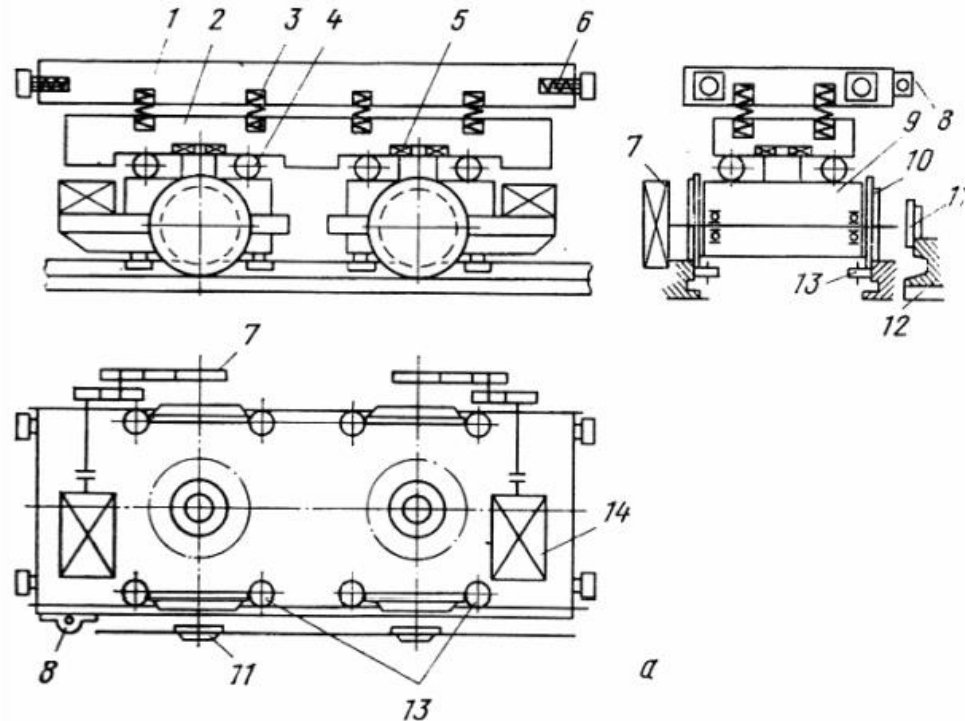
Злитковоз: 1 - платформа; 2 - плита; 3,6 -амортизатори; 4,5 - роликові підшипники; 7 - редуктор; 8 - підведення ел. енергії; 9 - ходові візки; 10 - колеса; 11 - холості бігунки; 12 - додаткова рейка; 13 - напрямні ролики; 14 - ел. двигун
